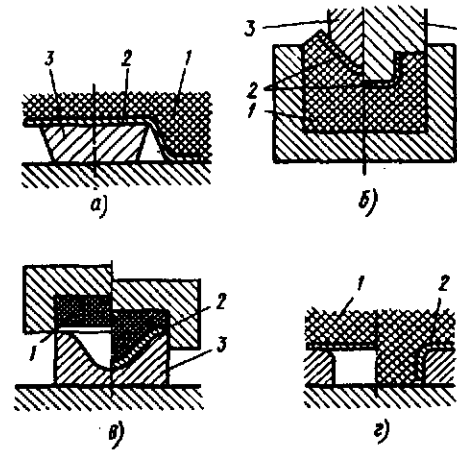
Схемы операции при штамповке с использованием полиуретана: а – вырубка; б – гибка в открытом и закрытом объеме; в – вытяжка; г – отбортовка; 1 – полиуретан; 2 – формируемая деталь; 3 – инструмент, формирующий деталь
